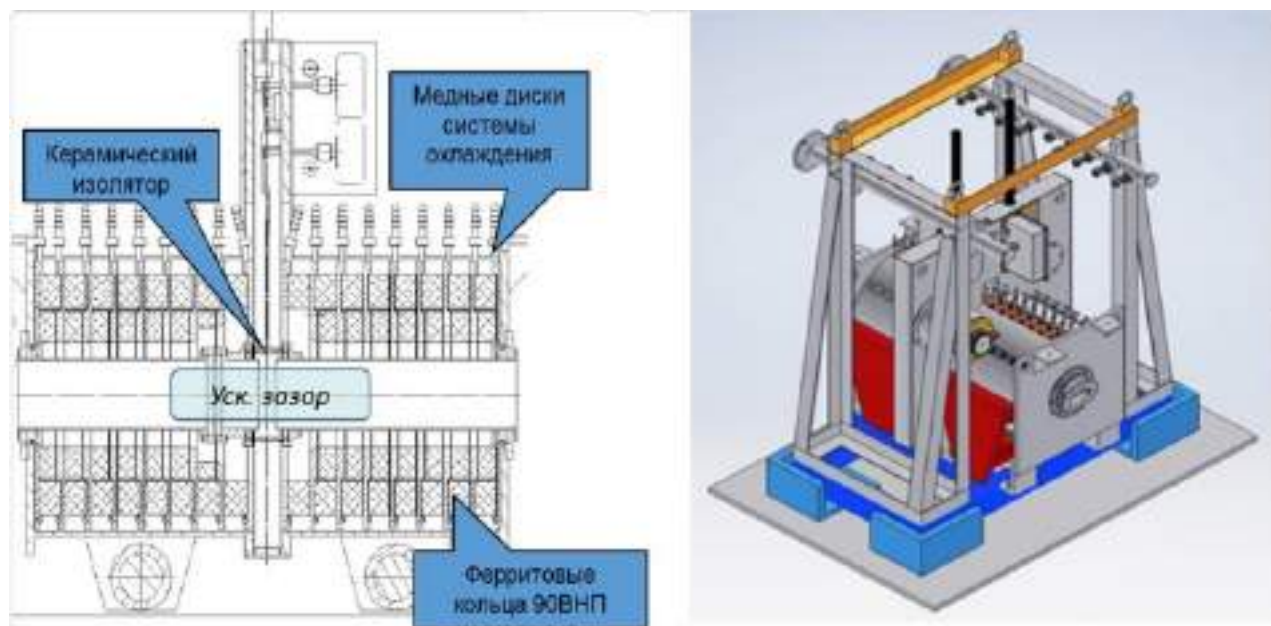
Схема резонатора новой ВЧ-системы (слева) и общий вид резонатора.
